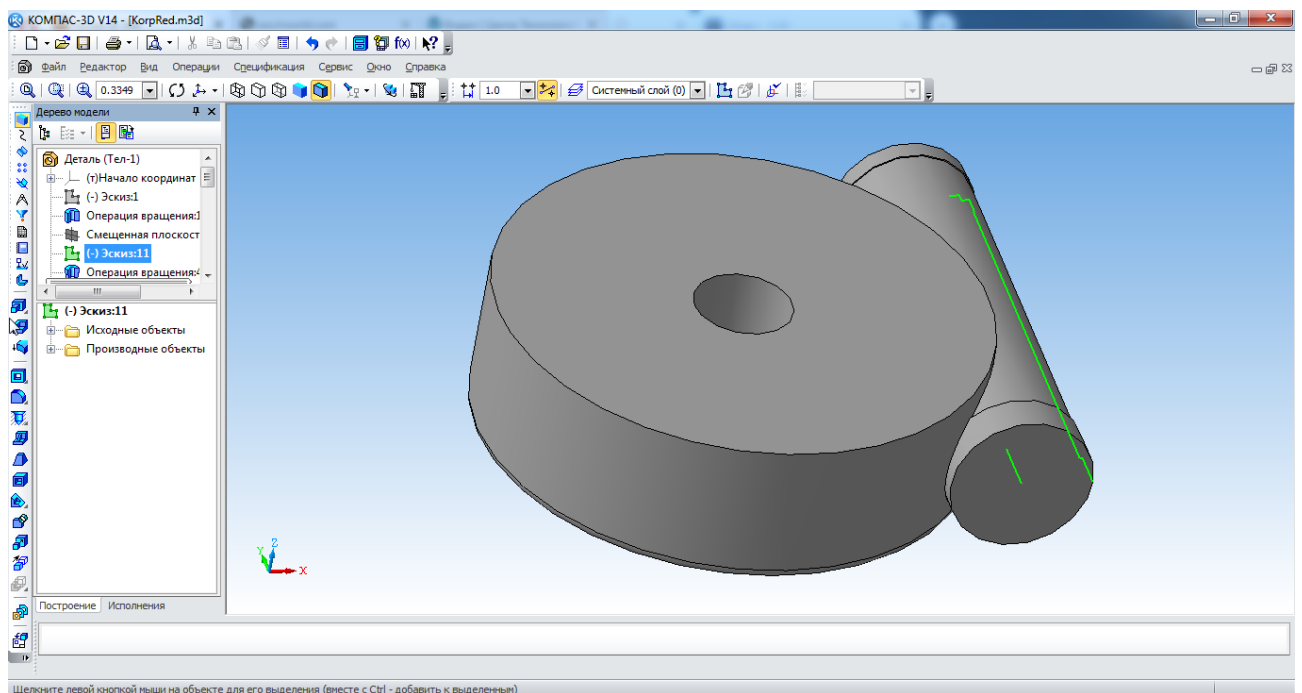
Долучення заготовки корпусу для черв'яка
